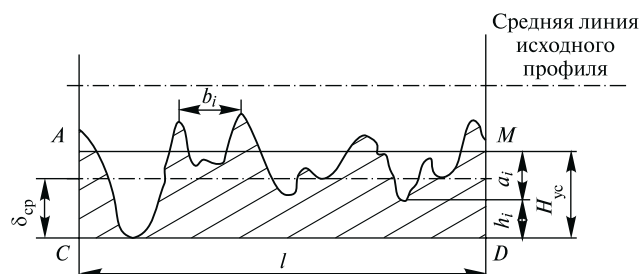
Схема образования профиля шероховатости поверхности при обработке свободными абразивами
